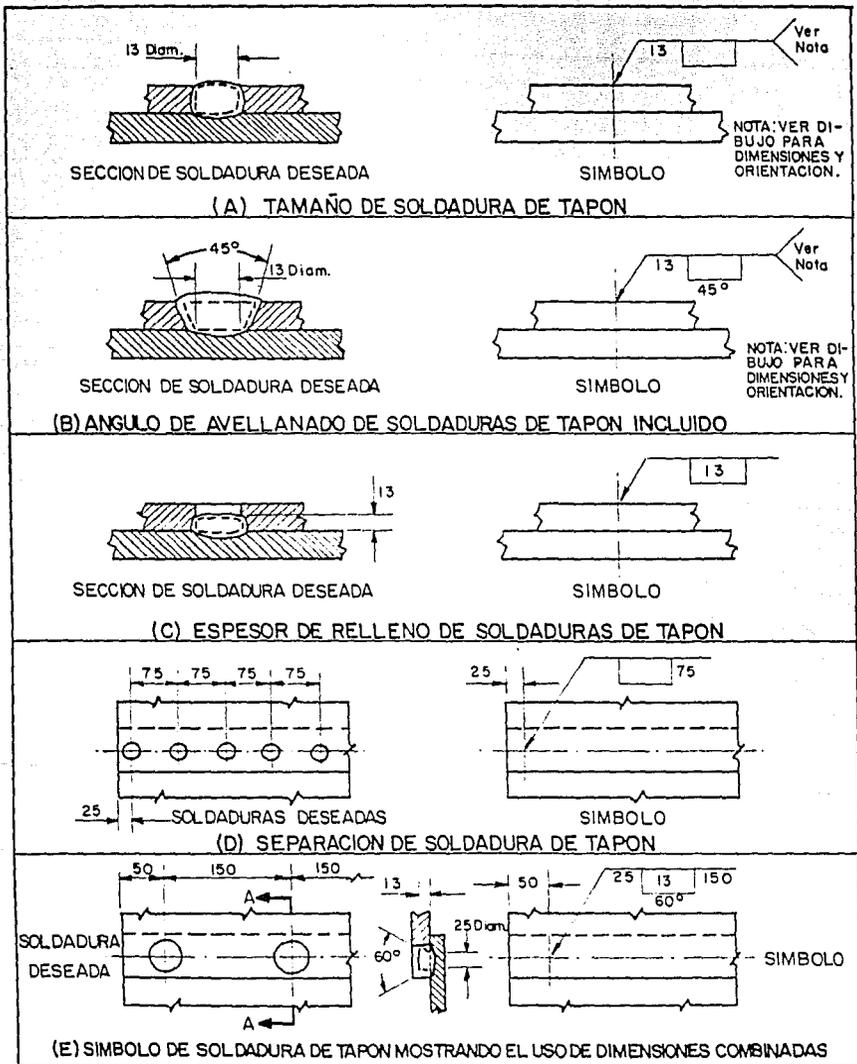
APLICACION DE DIMENSIONES PARA SIMBOLOS DE SOLDADURA DE TAPON
